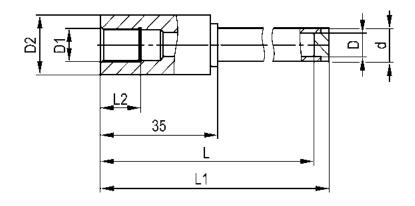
Гильза цилиндрическая резьбовая приварная OG3
